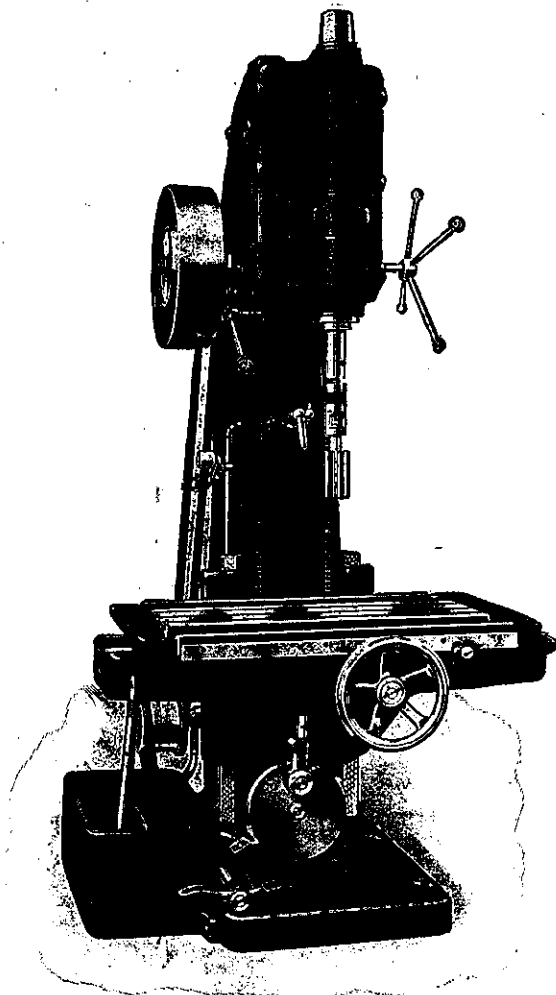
Zylinderpoliermaschine (Mayer & Schmidt)
